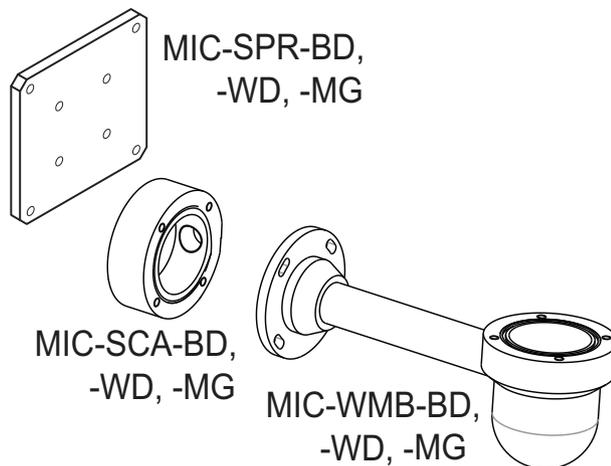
Configurazione tipica della staffa di montaggio a parete
